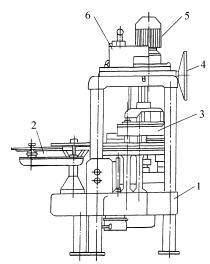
Машина для предварительной закатки банок 3П-10: 1 — станина; 2 — механизм подачи крышек; 3 — закаточное устройство; 4 — механизм ручного поворачивания машины; 5 — привод; 6 — коробка скоростей
